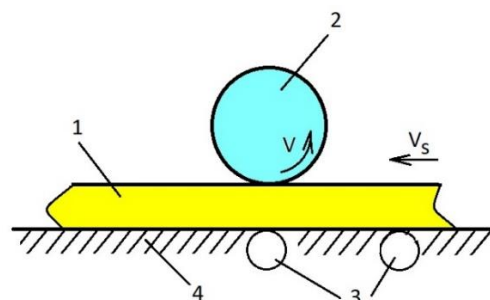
, б. Схема обработки на станке ШлПР: 1 – заготовка; 2 – шлифовальный круг; 3 – подающие вальцы; 4 – стол
